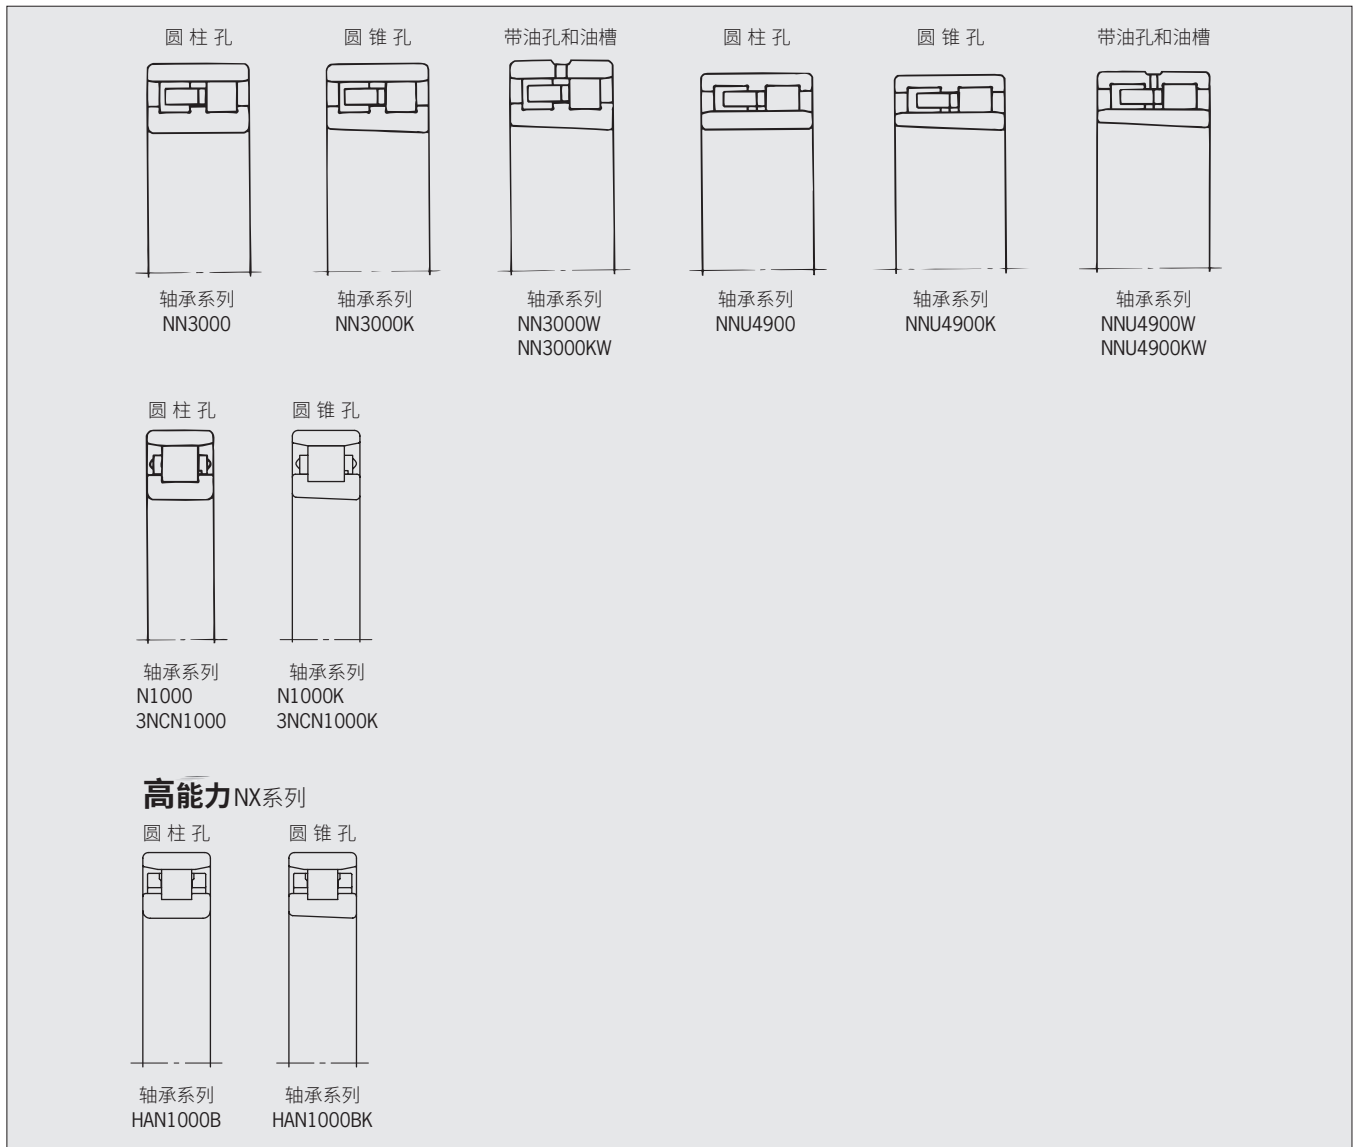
机床主轴用圆柱滚子轴承的形式和系列
